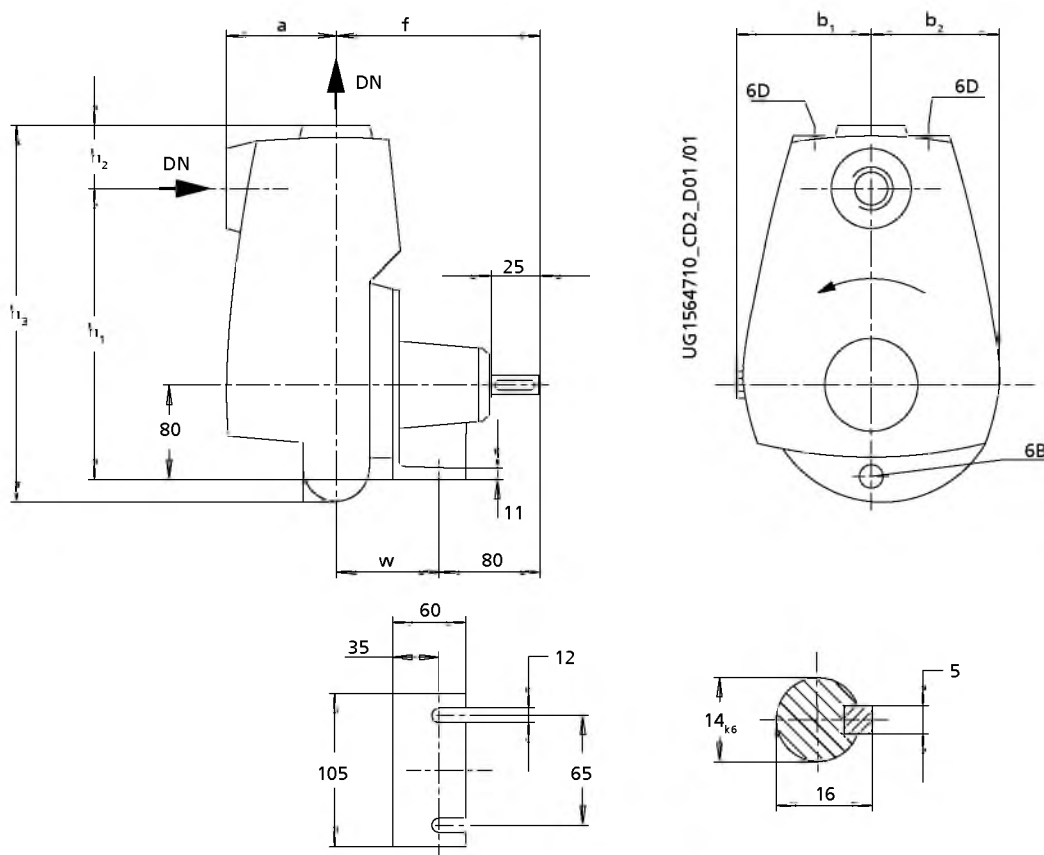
Габаритные размеры типоразмер 025-025-100 до 040-040-110 (узел вала 17) – насос
